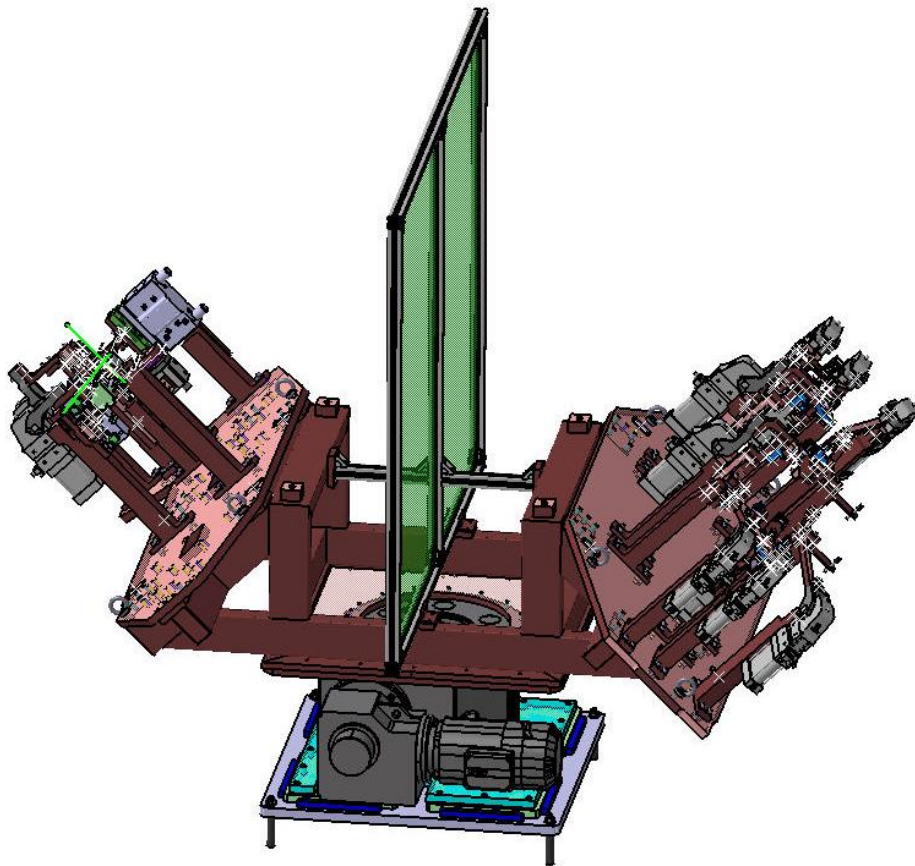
Estación doble de trabajo para soldadura por puntos (cortesía de INGEMAT SL)
